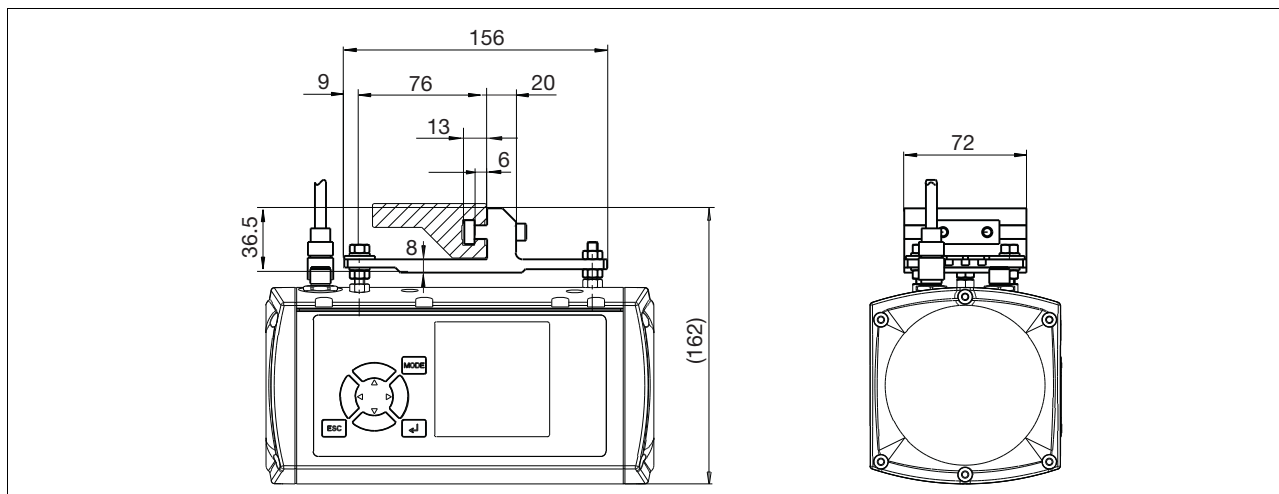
Abmessungen des Befestigungssatzes für den Empfänger, Maßangaben in mm
